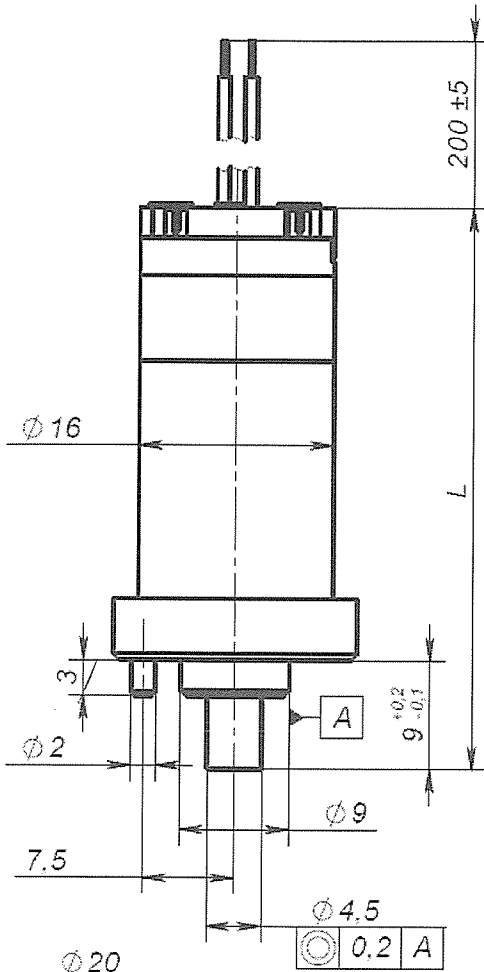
Габаритные и присоединительные размеры тензопреобразователя СХХП-1; исп. а и б.
